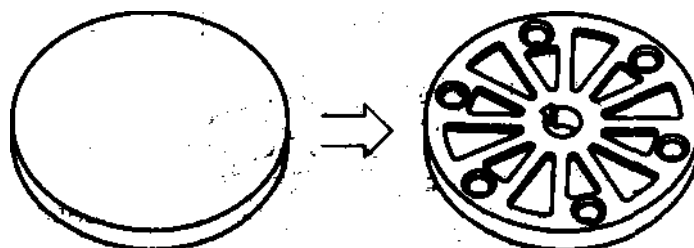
Використання циліндра як основи деталі (пластини)
